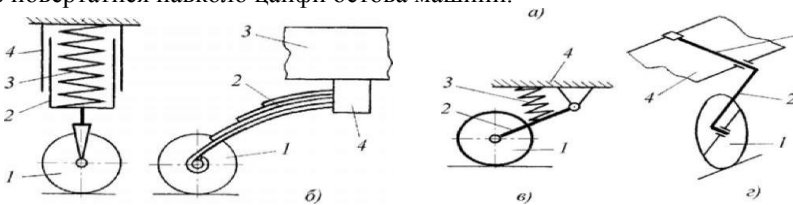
Схеми конструкцій індивідуальних підвісок гусеничних тракторів: *а* - «свічна»: 1 - опорний коток; 2 - стакан; 3 - пружина; 4 - напрямний циліндр; 5 - озов; *б* - ресорна: 1 - опорний коток; 2 - ресора; 3 - озов; 4 - кронштейн; *в* - важелева з пружиною: 1 - опорний коток; 2 - важіль; 3 - пружина; 4 - озов; *г* - важелева з торсіоном: 1 - опорний коток; 2 - важіль; 3 - торсіон; 4 - озов.
